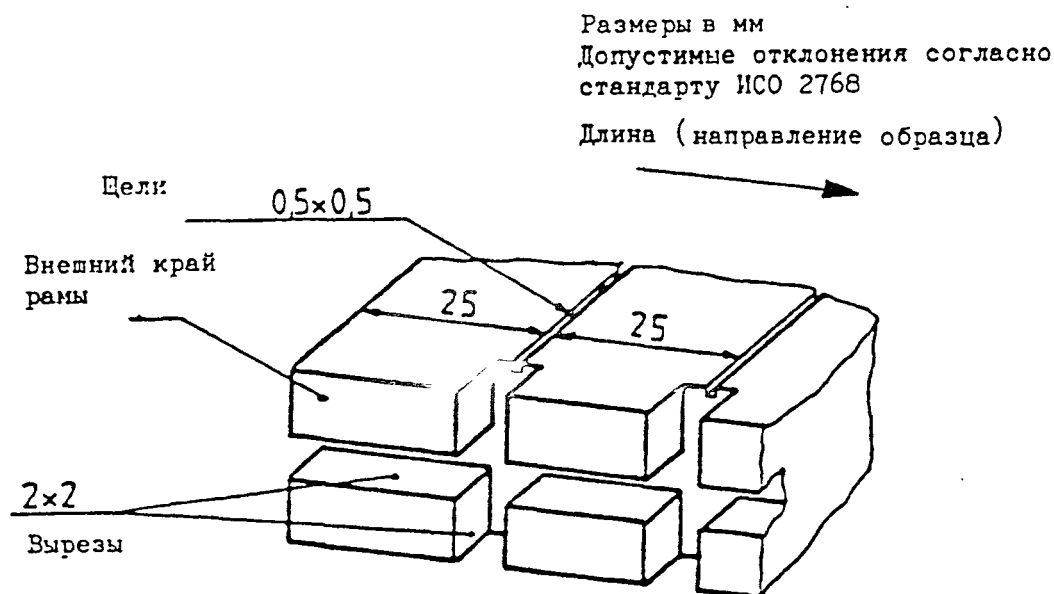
Образец части рамы в форме "U"; нижняя часть предусмотрена для натягивания проволоки
